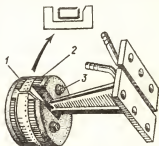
Индуктор с магнитной цепью для закалки внутренней цилиндрической поверхности непрерывно-последовательным способом:
